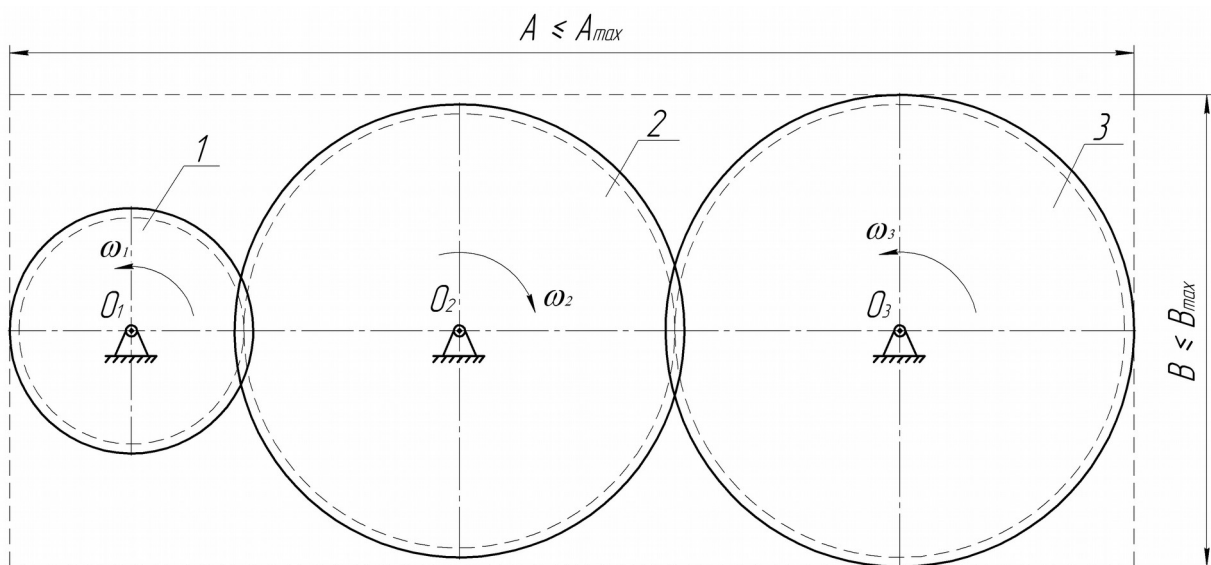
Кінематична схема рядового зубчатого механізму
